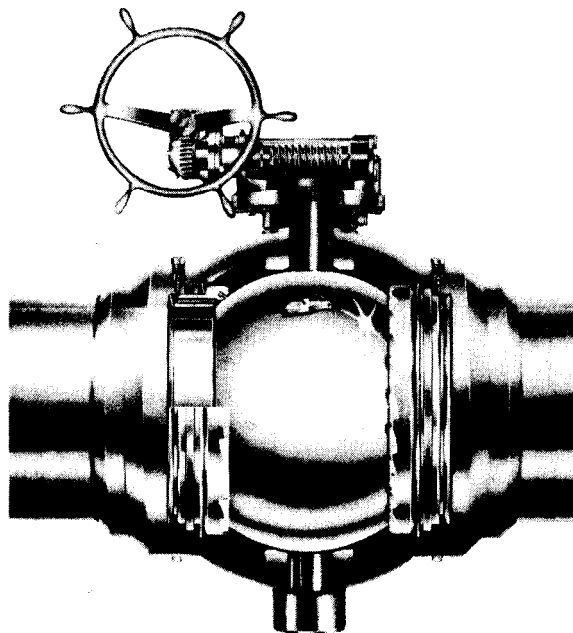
Válvula de bola montada en muñón con asientos giratorios
